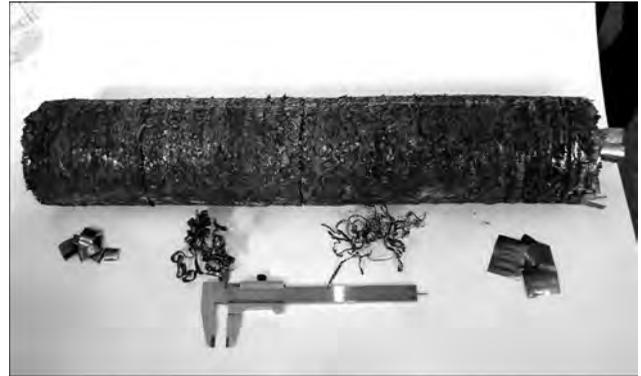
Заготовка, полученная из титановой стружки различных видов
